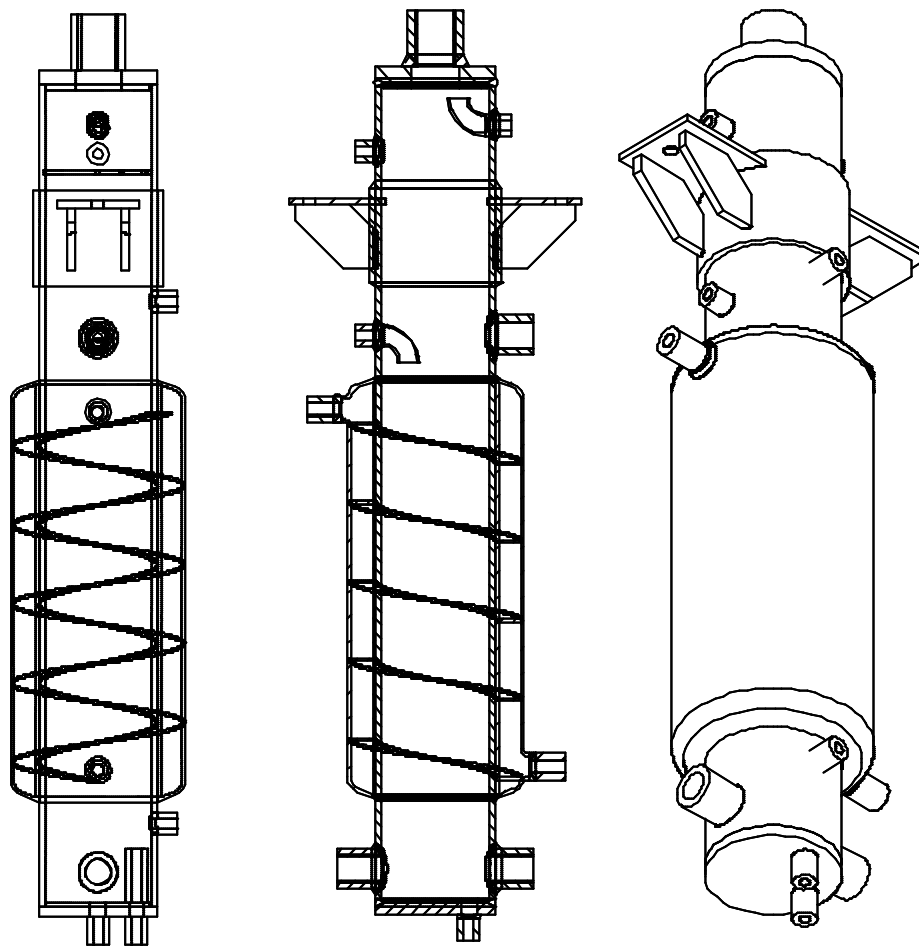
Der Mitteldruckabscheider, Querschnitt und 3D-Ansicht
